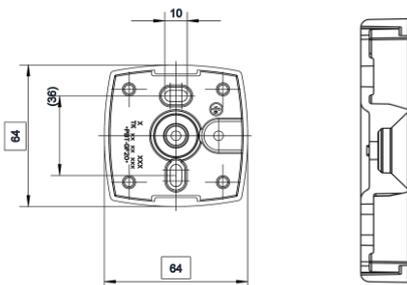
Vista dall'alto e sezione della piastra dell'adattatore
